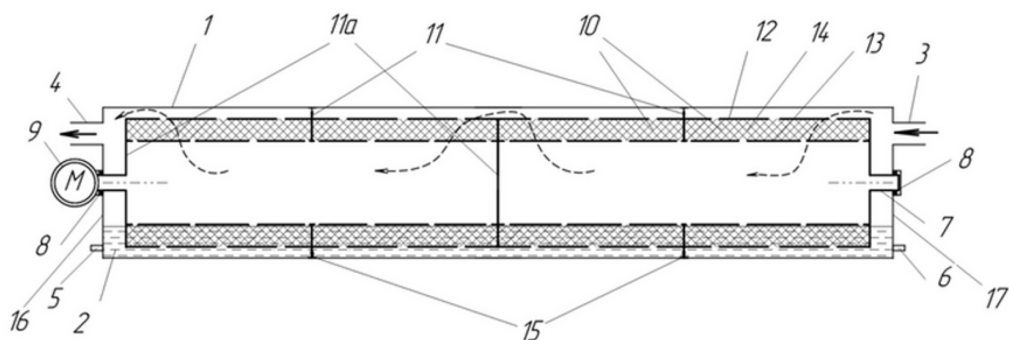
Горизонтальный насадочный тепло- и массообменный аппарат: 1 – цилиндрический корпус; 2 – жидкость; 3 – патрубок подвода газовой среды; 4 – патрубок отвода газовой среды; 5 – патрубок подвода жидкости; 6 – патрубок отвода жидкости; 7 – вал; 8 – подшипниковая опора; 9 – привод вращения; 10 – кольцевая насадочная конструкция; 11 – разделительная кольцевая перегородка; 11а – разделительная дисковая перегородка; 12 – внешняя коаксиальная перфорированная обечайка разного диаметра; 13 – внутренняя коаксиальная перфорированная обечайка разного диаметра; 14 – насадка; 15 – узел герметизации; 16 – днище; 17 – днище
